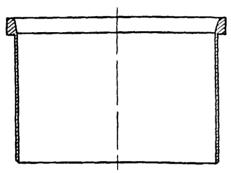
Приспособление для установки подвижного контакта камеры в корпус
